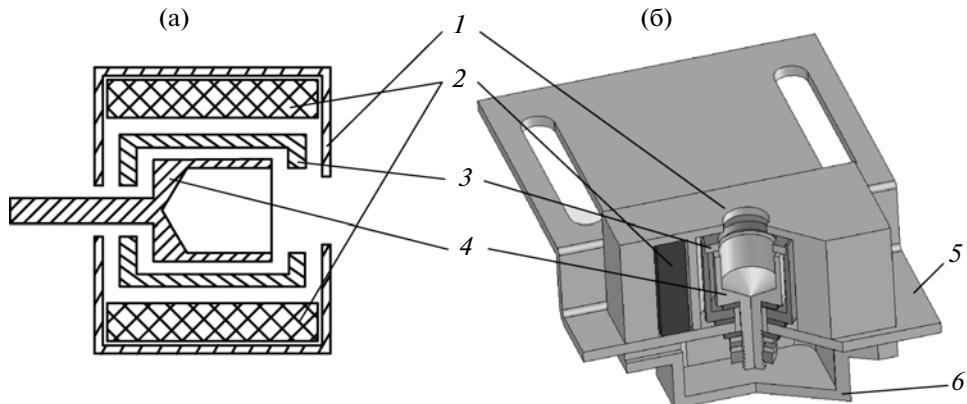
Схематичный разрез (а) и конструкция (б) устройства для регистрации заряженных частиц. 1 – корпус с входной диафрагмой; 2 – постоянные магниты; 3 – стакан с дополнительной диафрагмой; 4 – коллектор (цилиндр Фарадея); 5 – пластина для установки коллектора; 6 – задняя защитная крышка.
